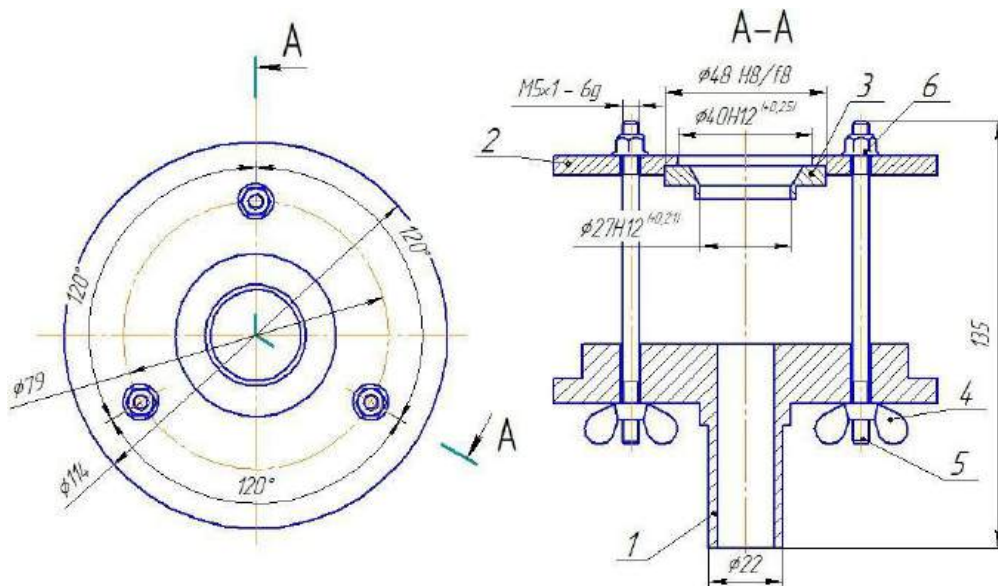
Кресленик пристосування для встановлення корпусу для напилювання.
